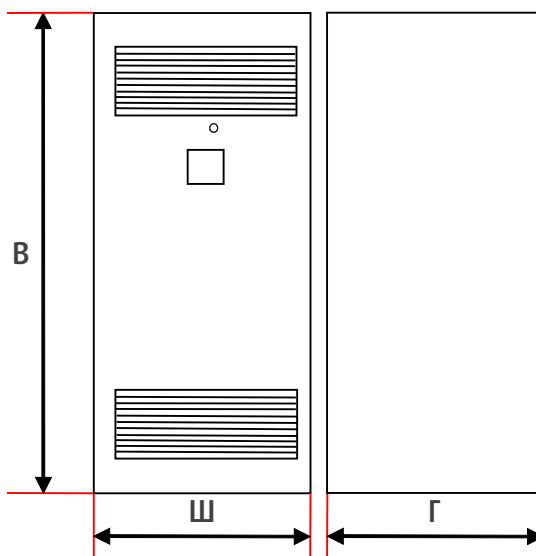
Габаритный чертеж установок ВАРНЕТ-НФ.
